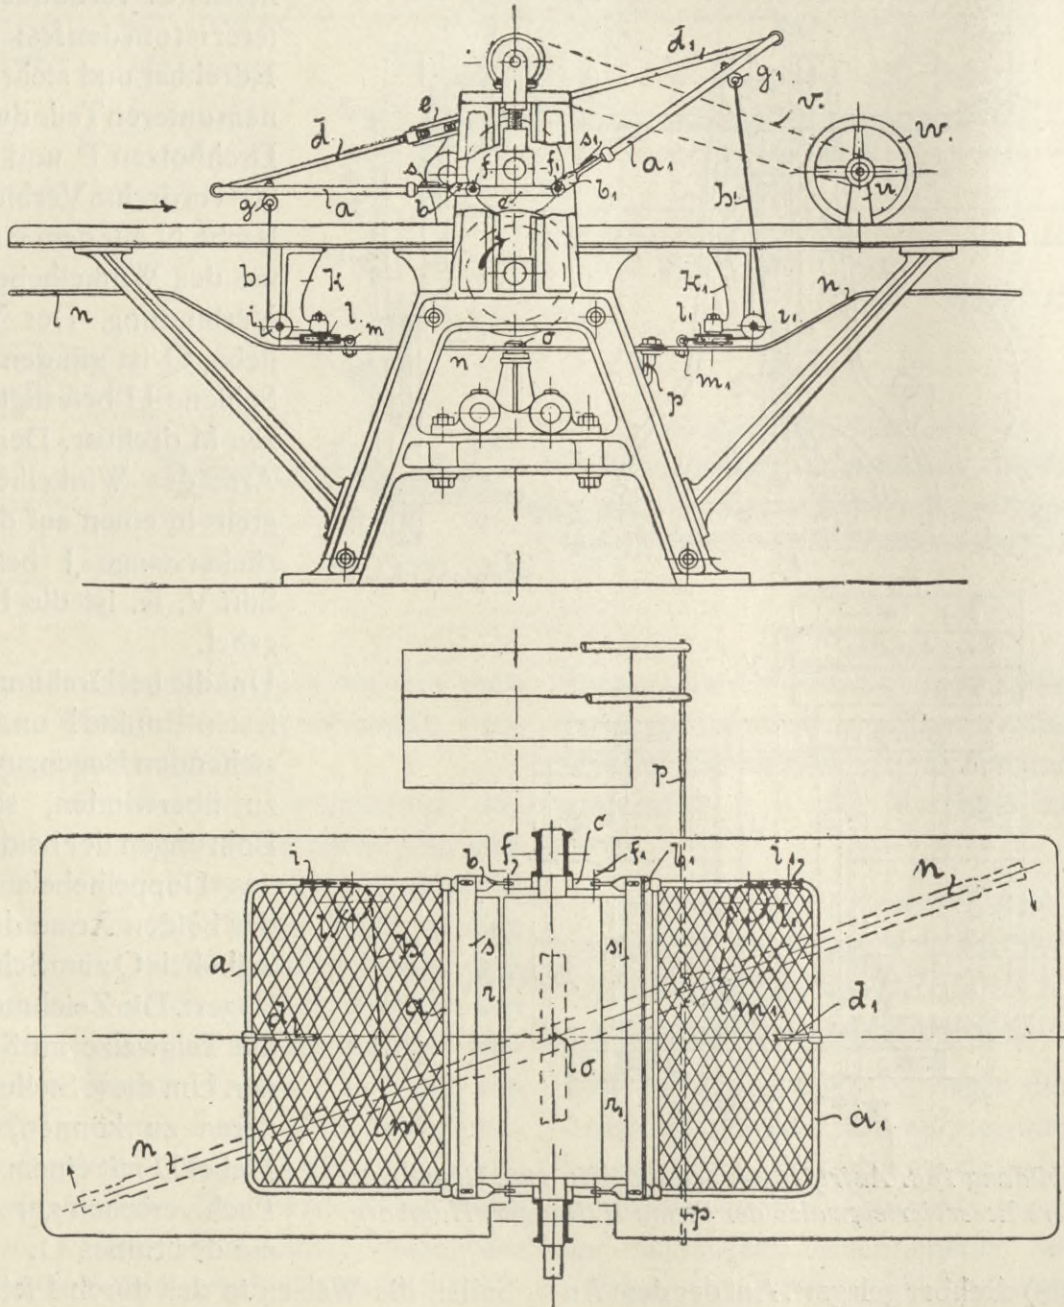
Aufriß, 192. Grundriß. Ältere Reversierteigwalze der Firma Rudolf Scheffus, Hamburg.
